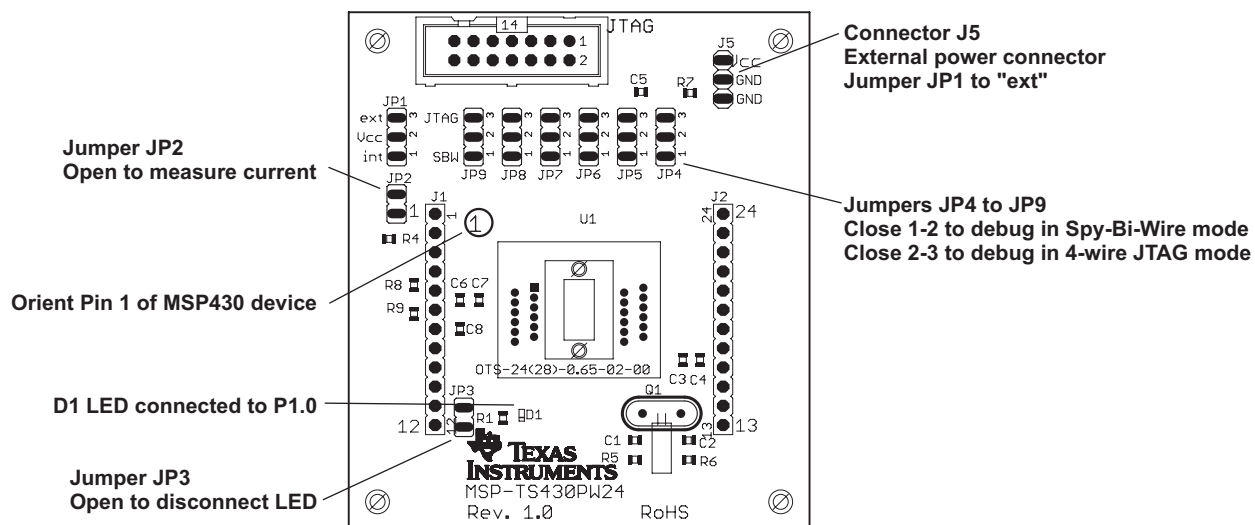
MSP-TS430PW24 目标插座模块, PCB
